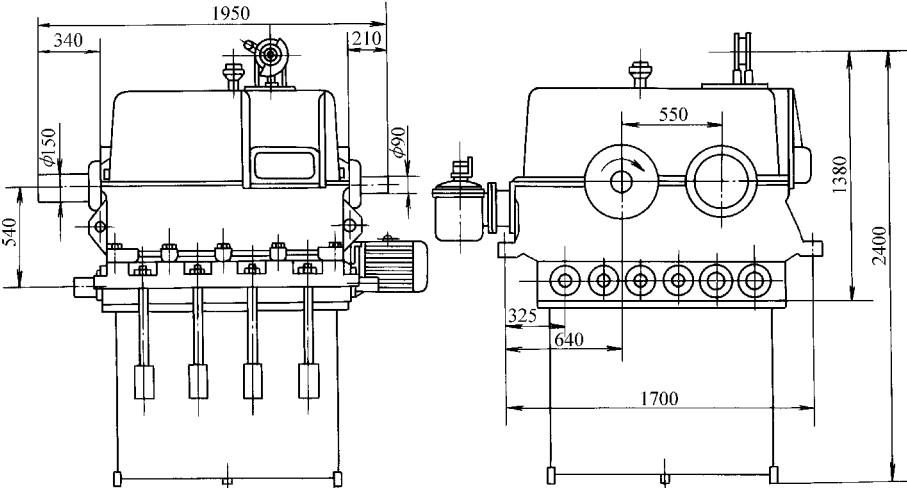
2-33 YOCF-01 型液力偶合器传动装置外形简图
